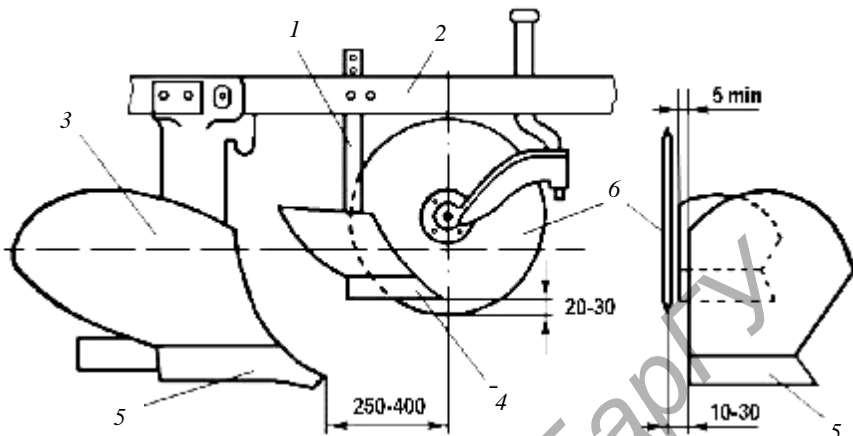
Установка предплужника и ножа на раме плуга:
